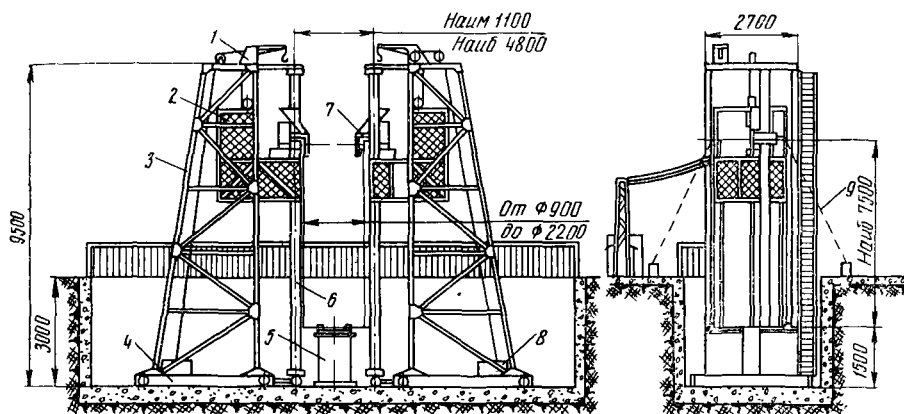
Установка для электрошлаковой сварки продольных швов
